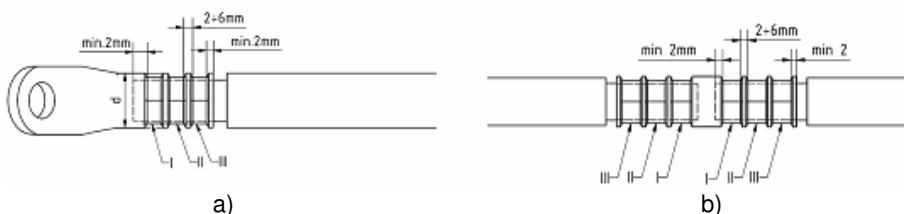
Способ запрессовывания а) трубный наконечник б) трубный соединитель
